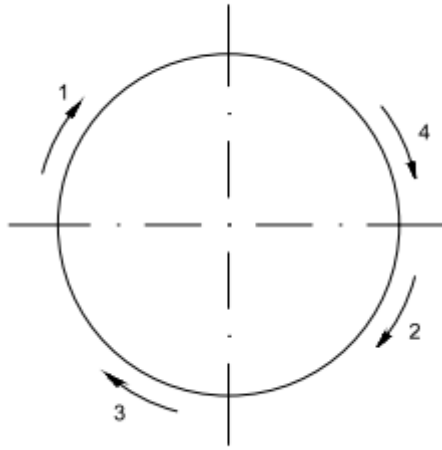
Послідовність зварювання обшивки з прутком
